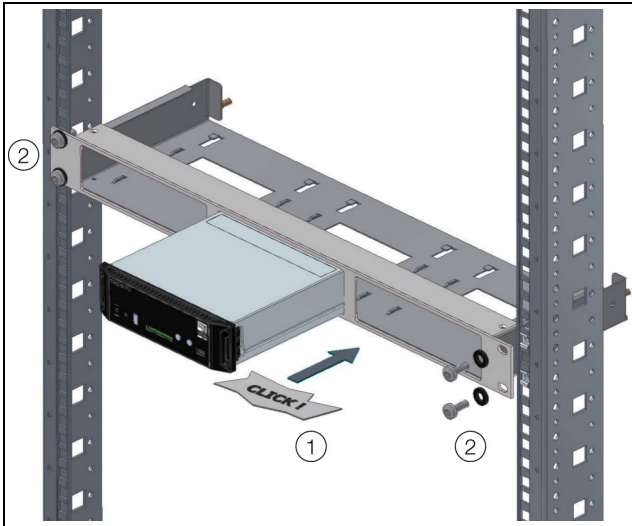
Befestigen der Montageeinheit in einem Einschub
